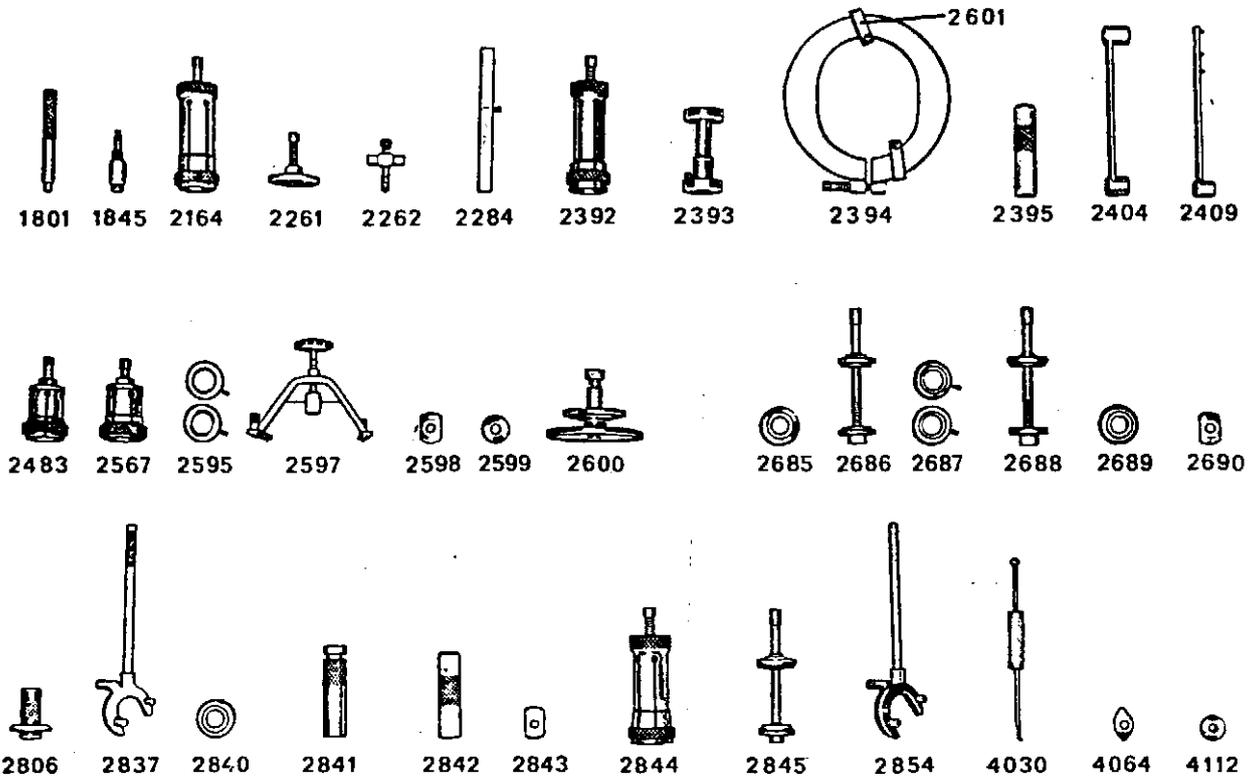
Spezialwerkzeuge für Hinterachsgetriebe
